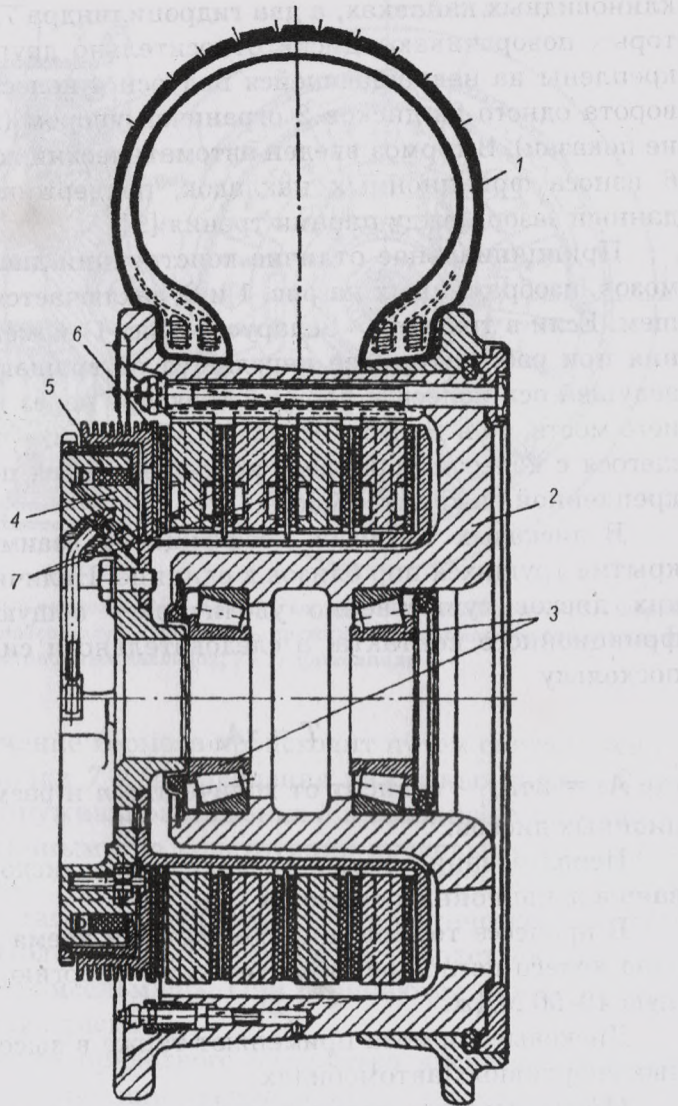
Тормозное колесо самолета: 1 – шина; 2 – корпус колеса; 3 – подшипник; 4 – корпус тормоза; 5 – тормозной цилиндр с поршнем и уплотнителем; 6 – нажимной диск; 7 – фрикционный диск
